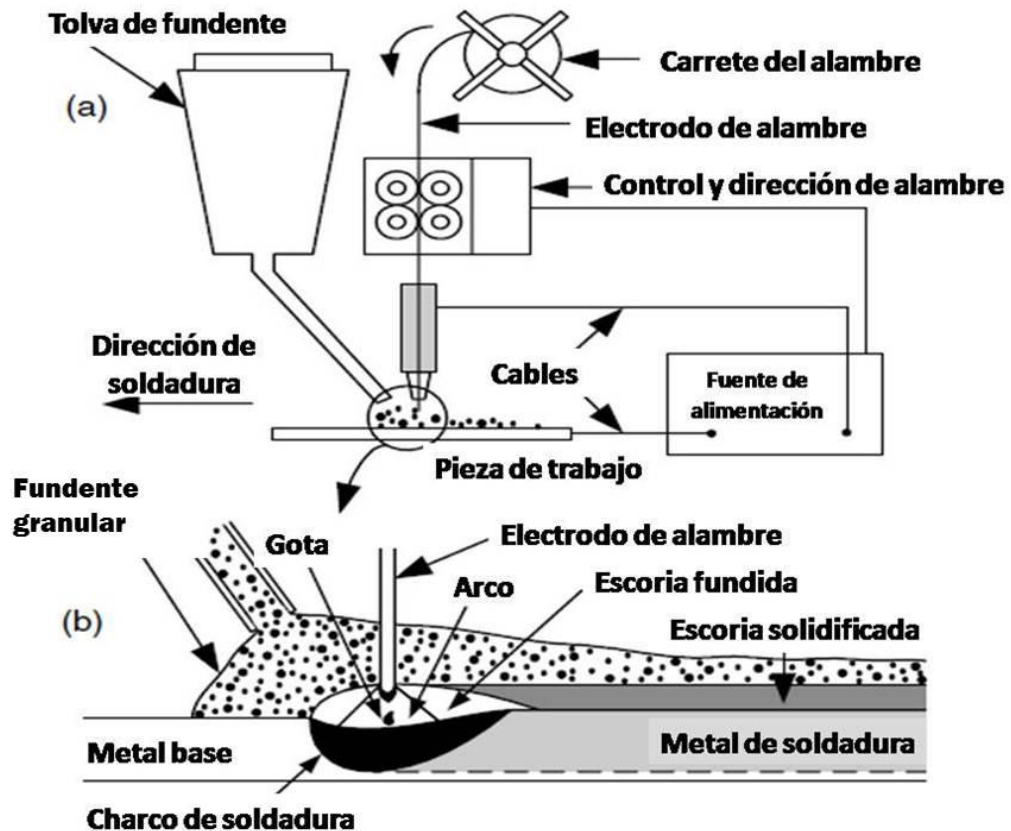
1 Soldadura por arco sumergido: (a) Proceso general; (b) Área de soldadura ampliada (31).
